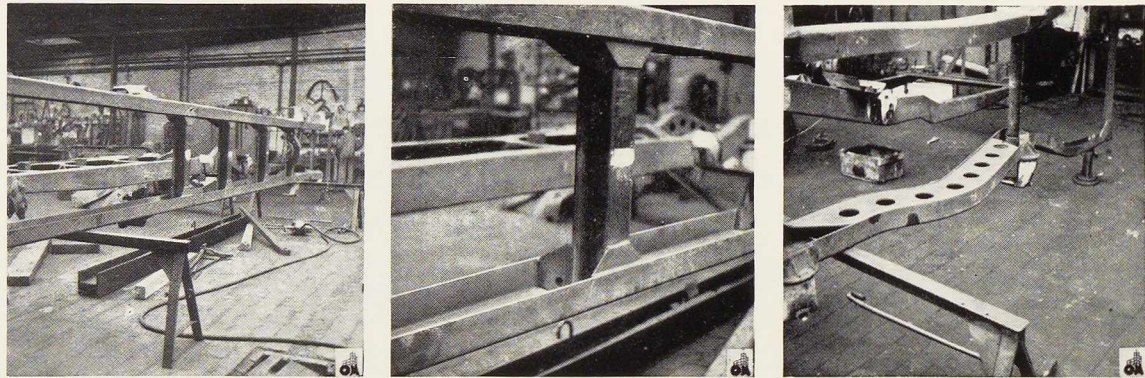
Vue générale d'un châssis d'autocamion disposé verticalement en cours de montage en vue de sa construction soudée. — Détail du nœud d'assemblage d'une entretoise soudée sur la membrure. — Détail de la conception de la partie arrière renforcée de la membrure constituée en forme de poutre en caisson.
